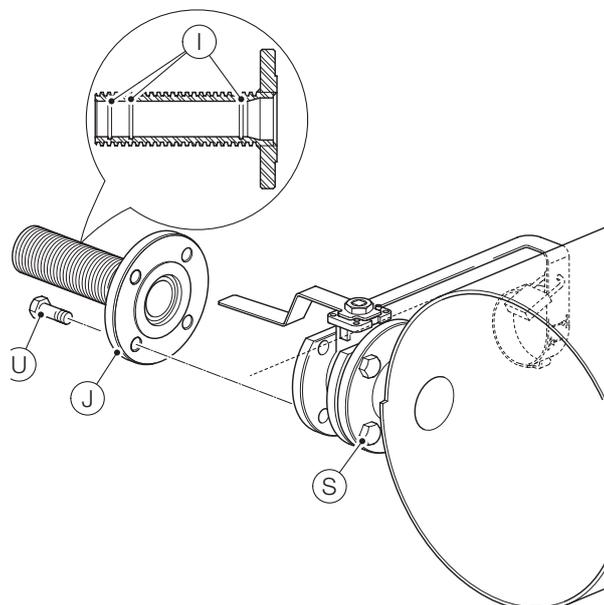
O-Ringe im Gewindeadapter auswechseln
